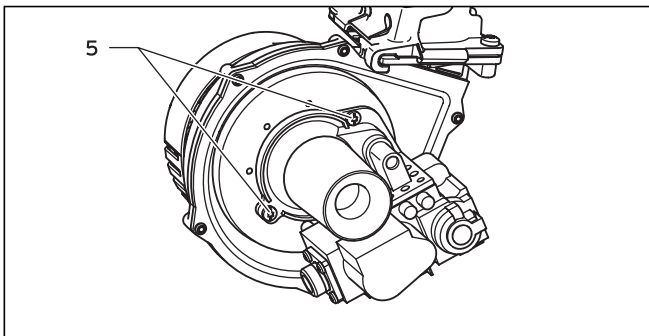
Vissage mécanisme gaz/ventilateur
